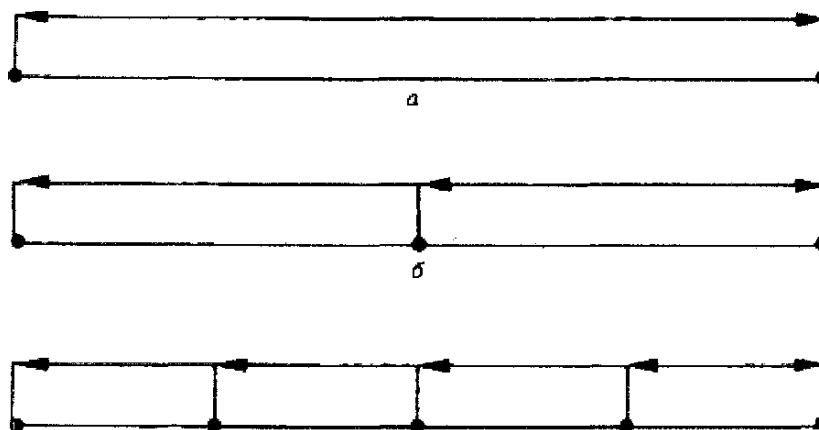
Различные схемы сварки: а— сварка напроход;. б — сварка от середины к краям; в - обратноступенчатый способ
